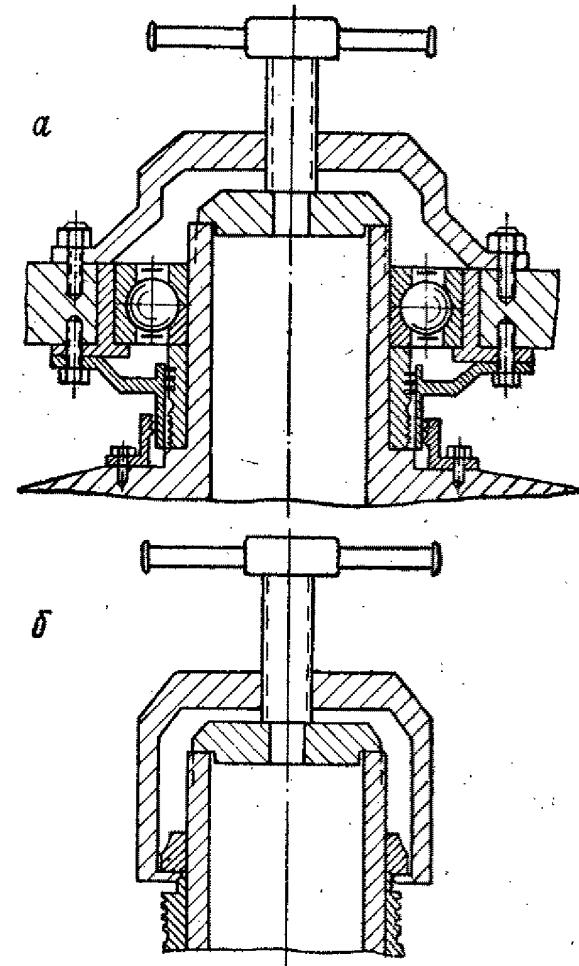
Схема демонтажа шарикоподшипника с разъемным внутренним кольцом:
